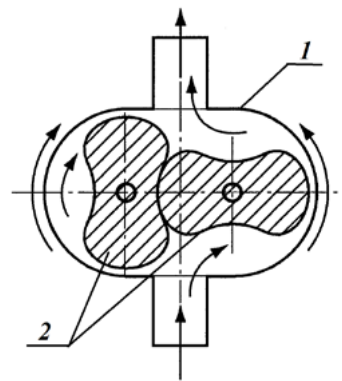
Схема нагнетателя восьмерочного типа: 1 — корпус, 2 — рабочее колесо
